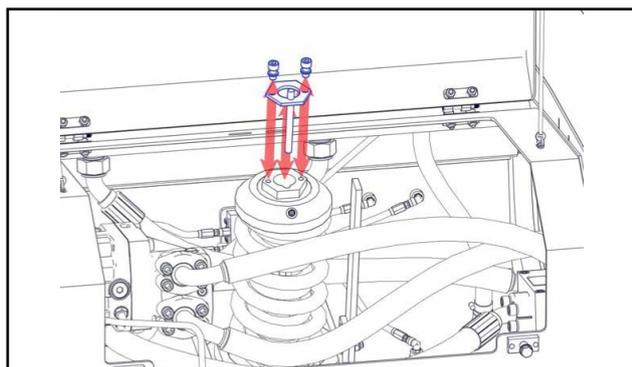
Пластина механизма рычажного типа: Демонтаж стопорной пластины
